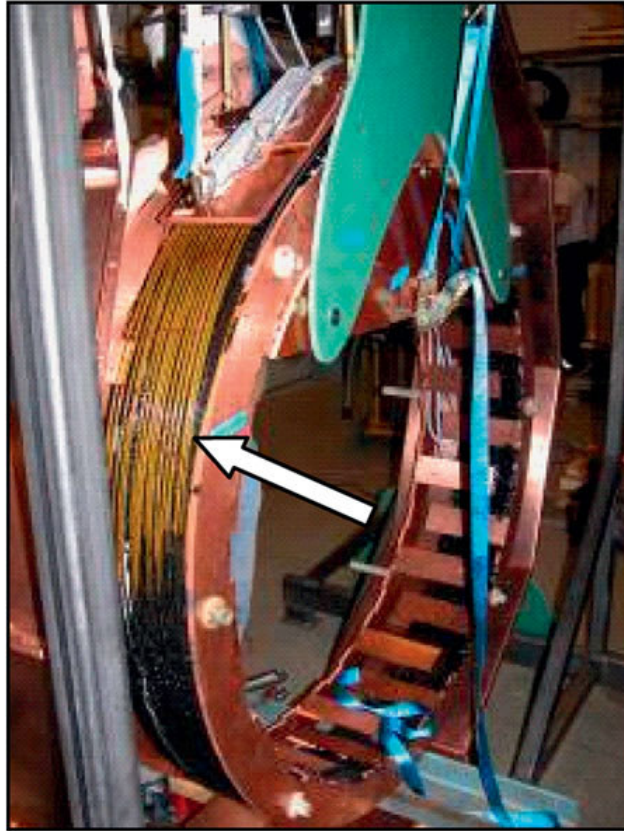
Calentador de inducción con bobina de  $MgB_2$  (indicada por la flecha) antes ser ingresada en su cámara de vacío para prueba.
